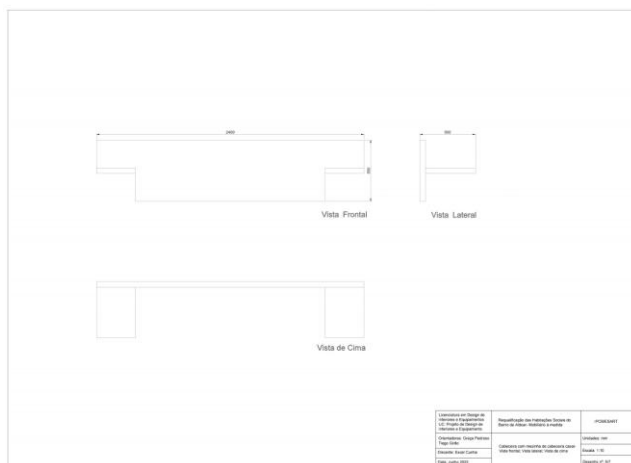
Desenho de conjunto da cabeceira, 150cm.
